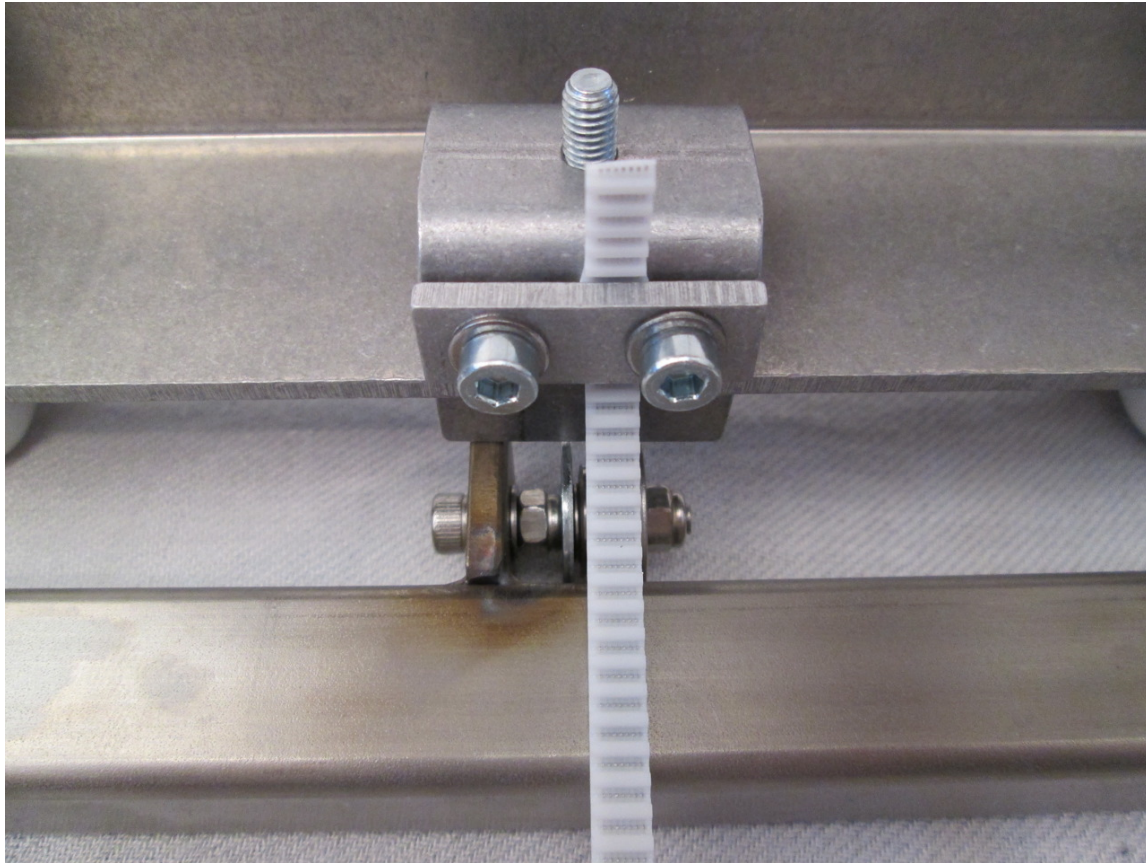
Zahnriemenführung Detailansicht Verschraubung
